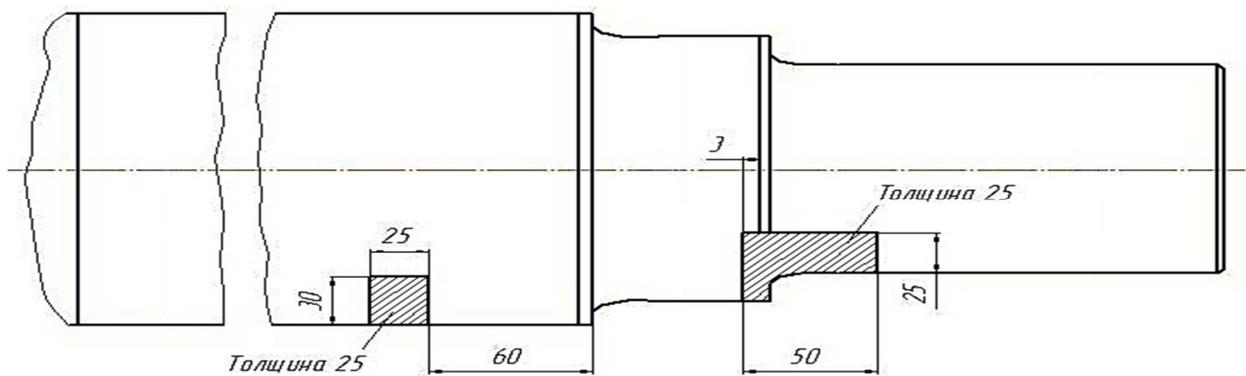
Схема вырезки шлифов из подступичной части и шейки оси
